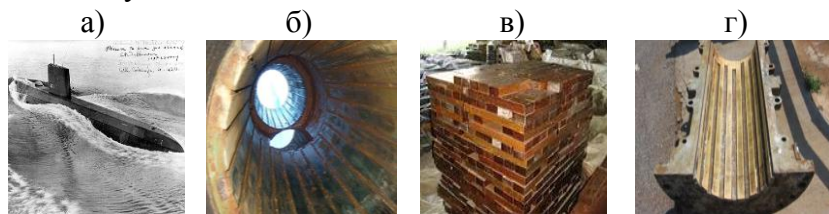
Подлодка (а), подшипник гребного вала (б), заготовки для набора подшипника (в), полувкладыш (г)
